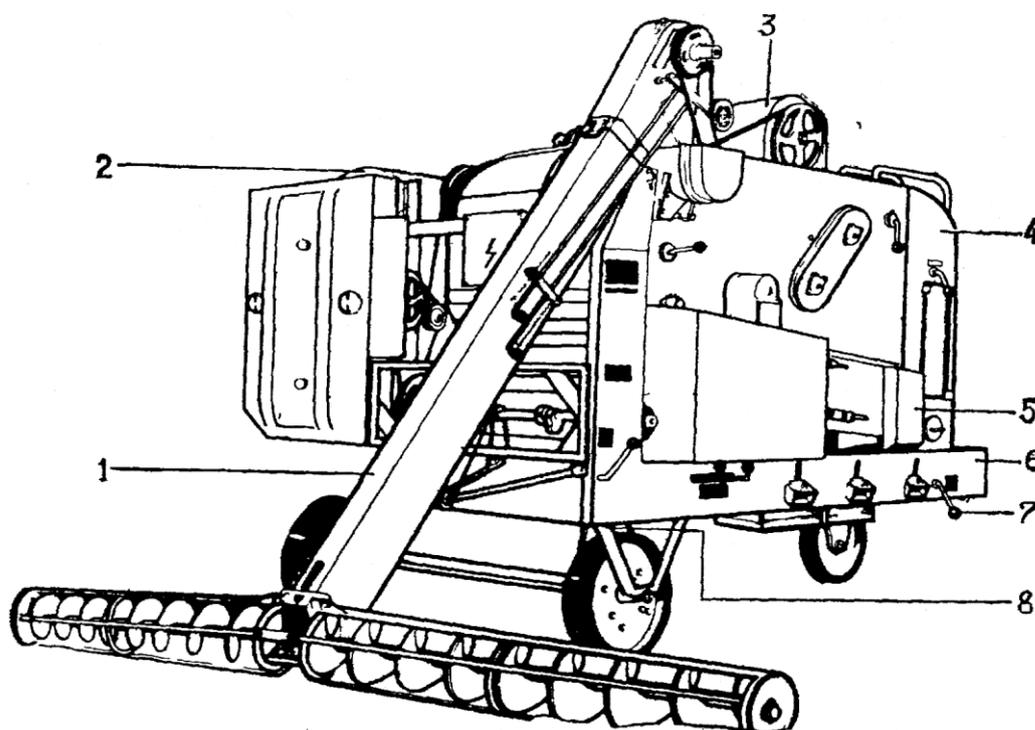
Общий вид машины: 1 - загрузочный транспортер с питателями; 2 - триерные цилиндры; 3 - элеватор; 4 - воздушно-очистительная часть; 5 - решетный стан; 6 - рама; 7 - шнек чистого зерна; 8 - механизм самопередвижения
